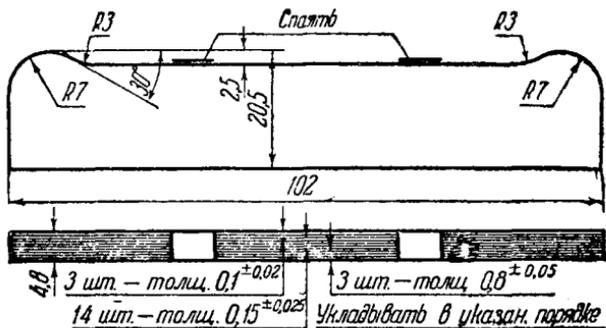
Дет. № 0324. Прокладка переднего коренного подшипника регулировочная
